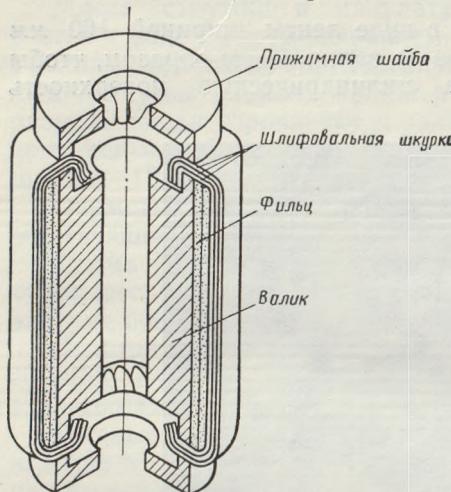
Шлифовальный валик для шлифования обечеек корпуса гитары
